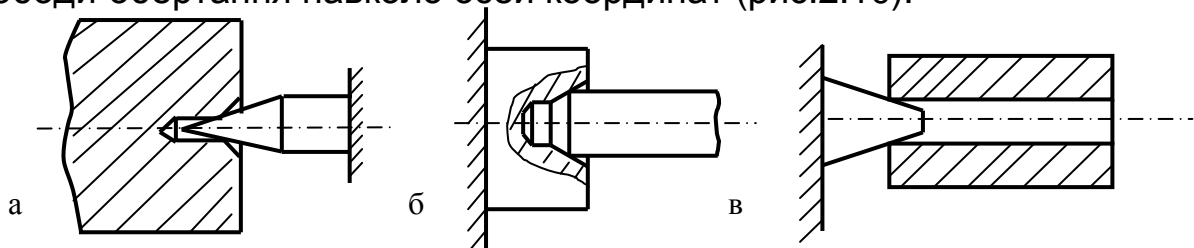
Установлення на конус заготовок: а, б- валів ; в- втулок та труб.
